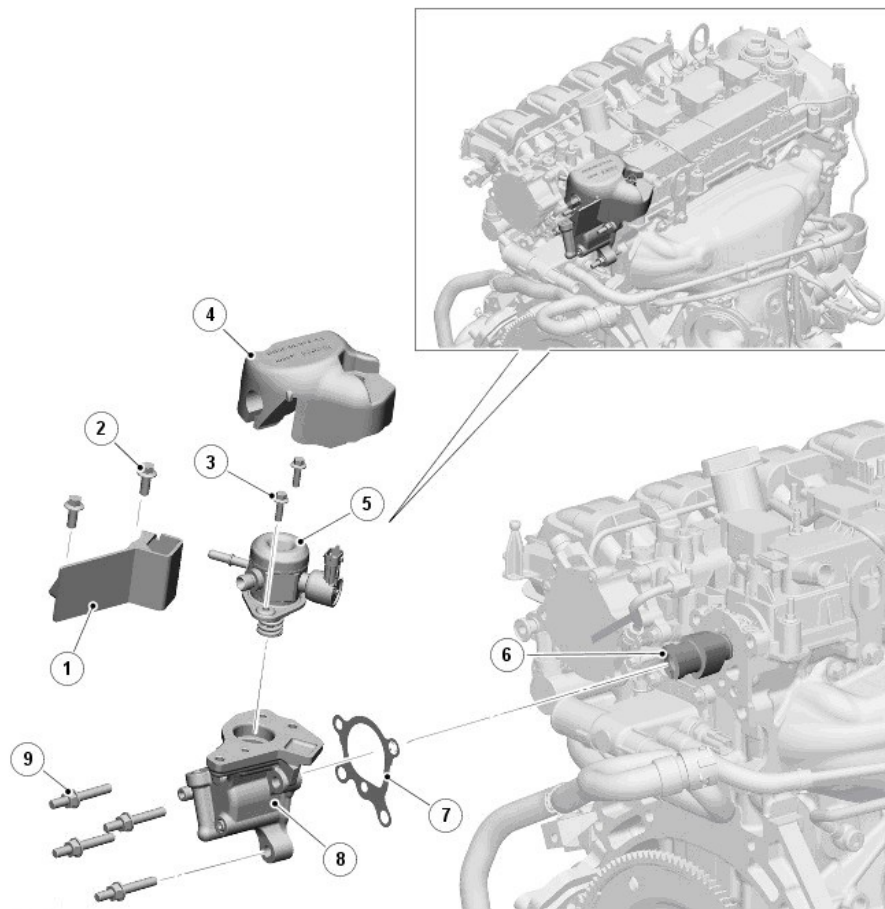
Топливный насос высокого давления бензинового двигателя 2.0L GTDi.
